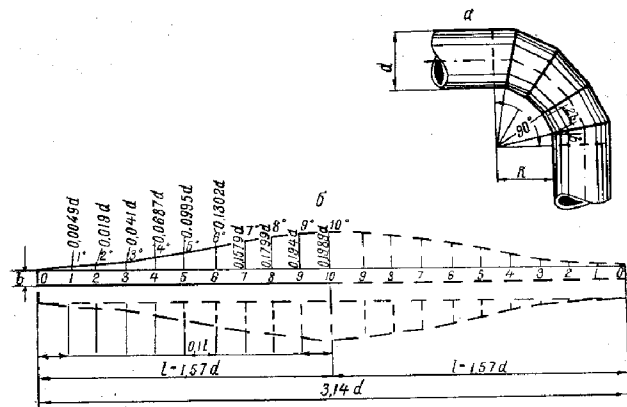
Сварной отвод 90°, состоящий из трех звеньев и двух стаканов.
